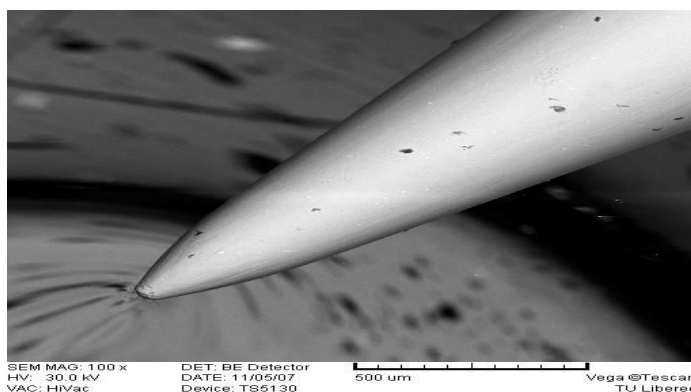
Detail hrotu jehly s chromovým povlakem (po 5 pracovních směnách)
